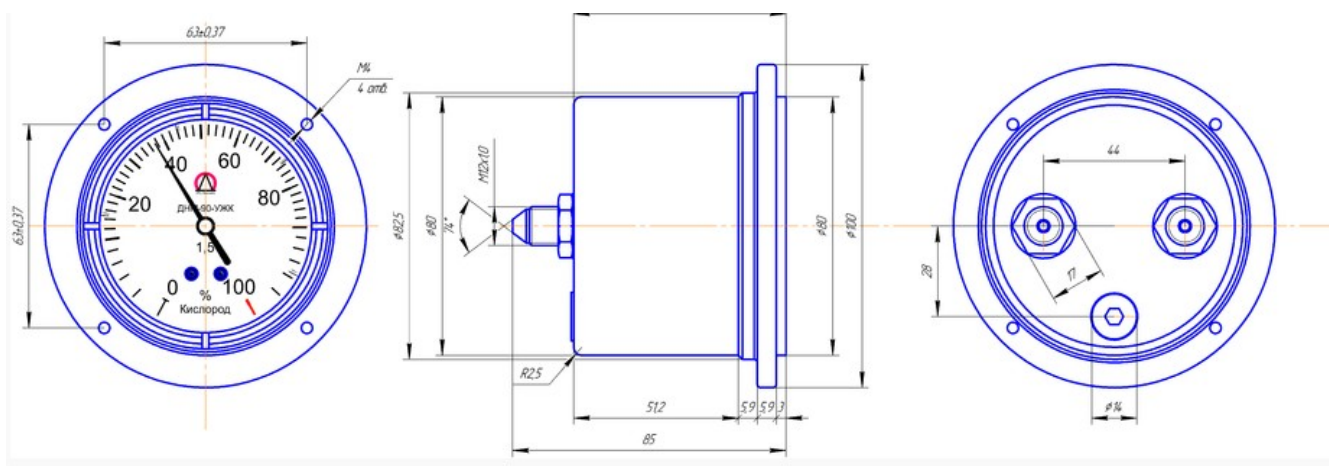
Габаритные и присоединительные размеры Дифманометра- напоромера ДНМ - 90
